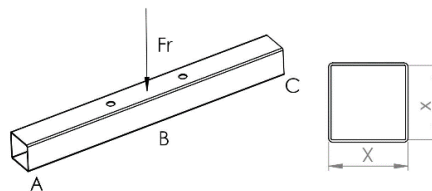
Esfuerzo crítico en elemento 6 de la estructura
